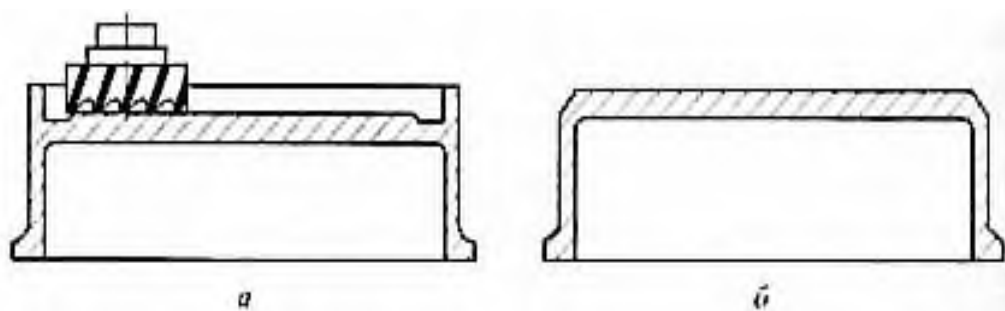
Обработка заготовок корпусных деталей за один проход [7]
